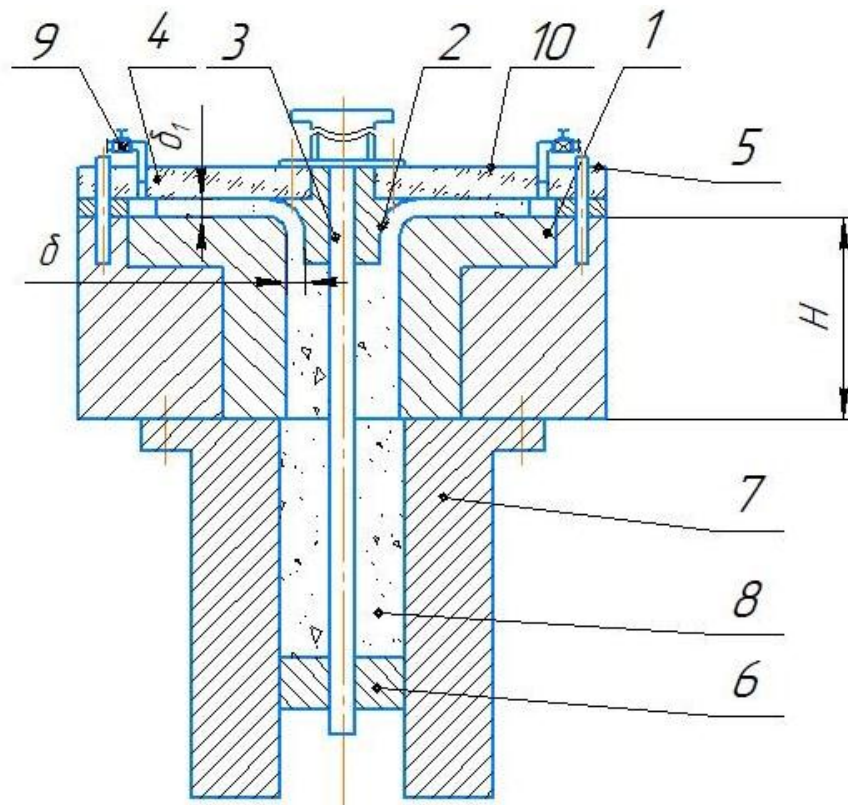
Пристрій для визначення форм і розмірів заготовки для витяжки деталей різної форми:
